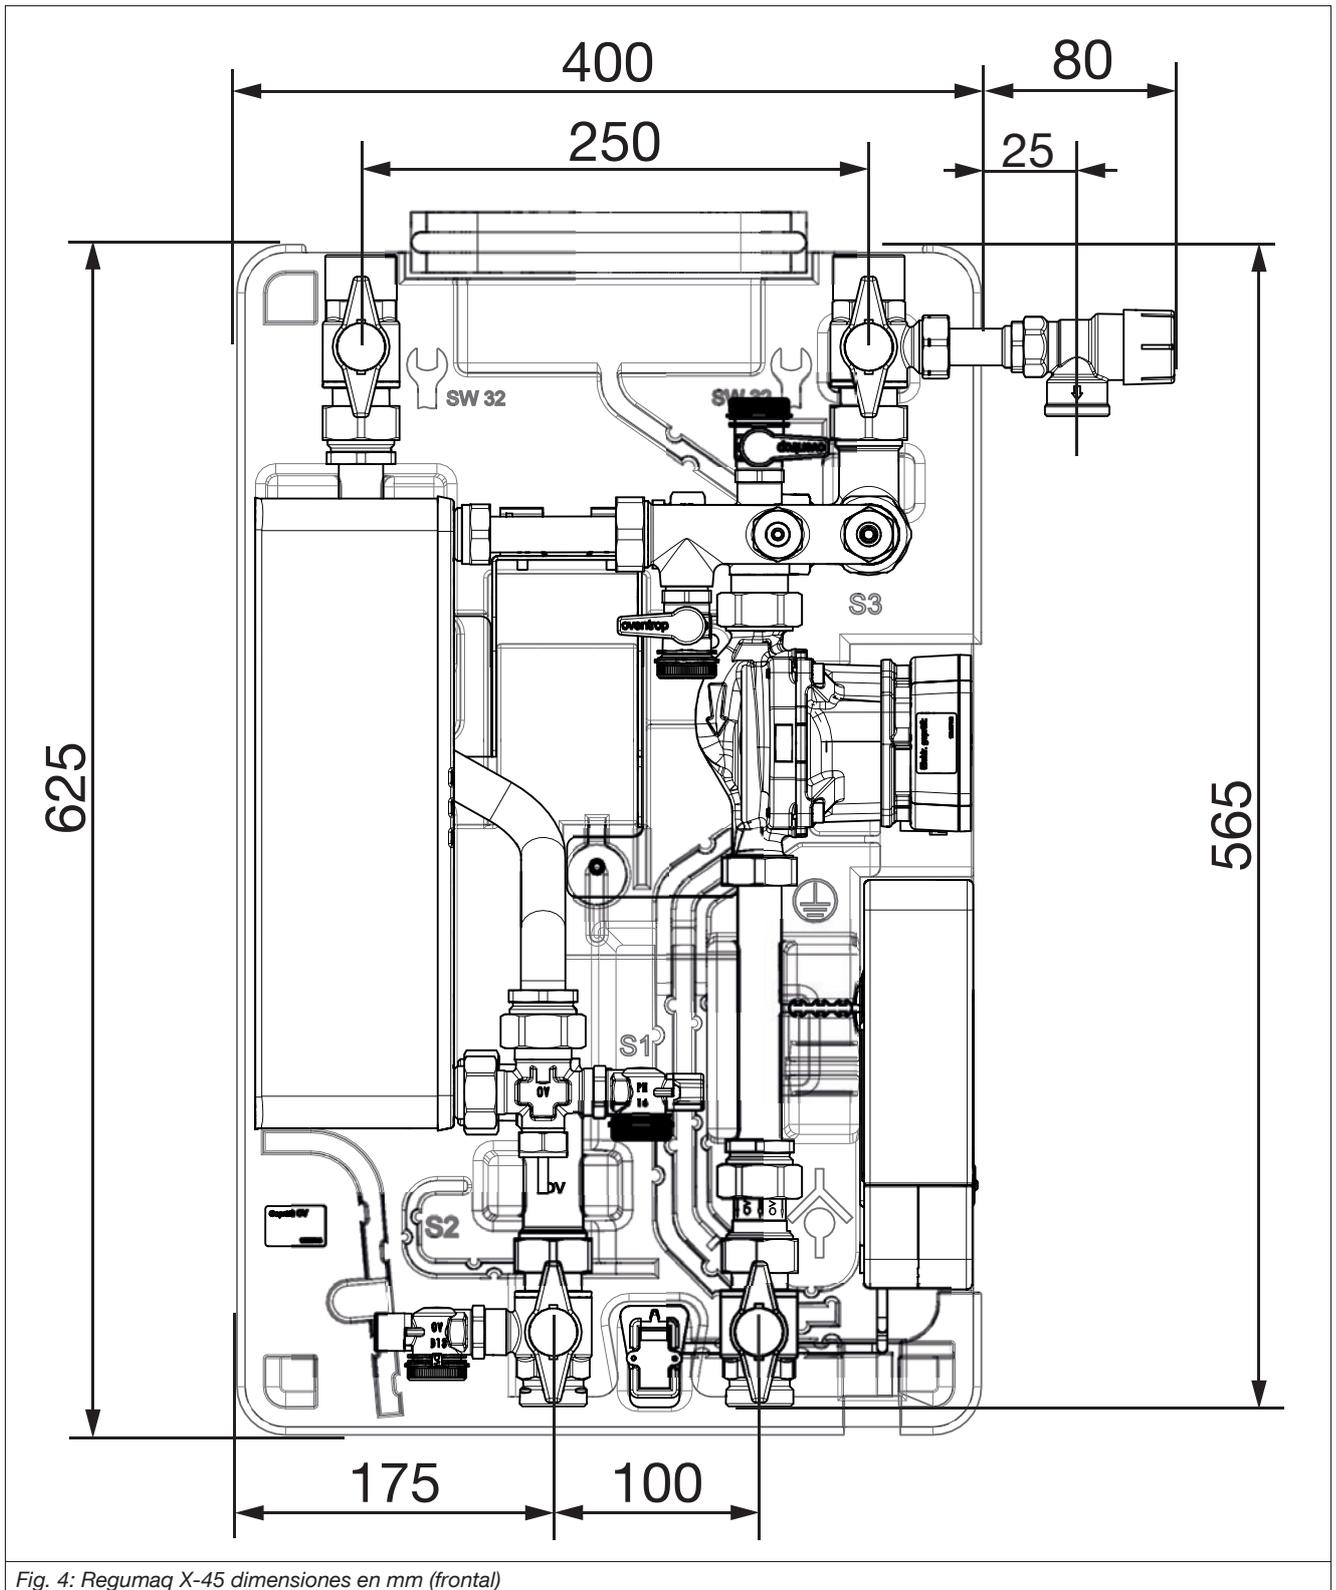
Regumaq X-45 dimensiones en mm (frontal)
